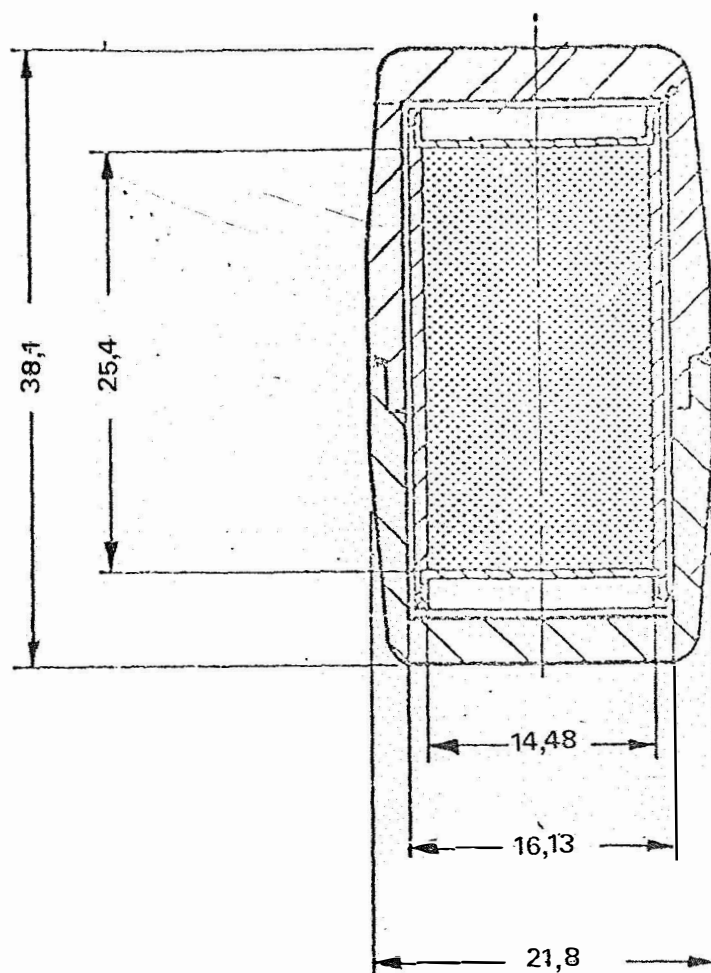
Esquema da cápsula de ^{60}Co - 316 L (dimensões em milímetros).
